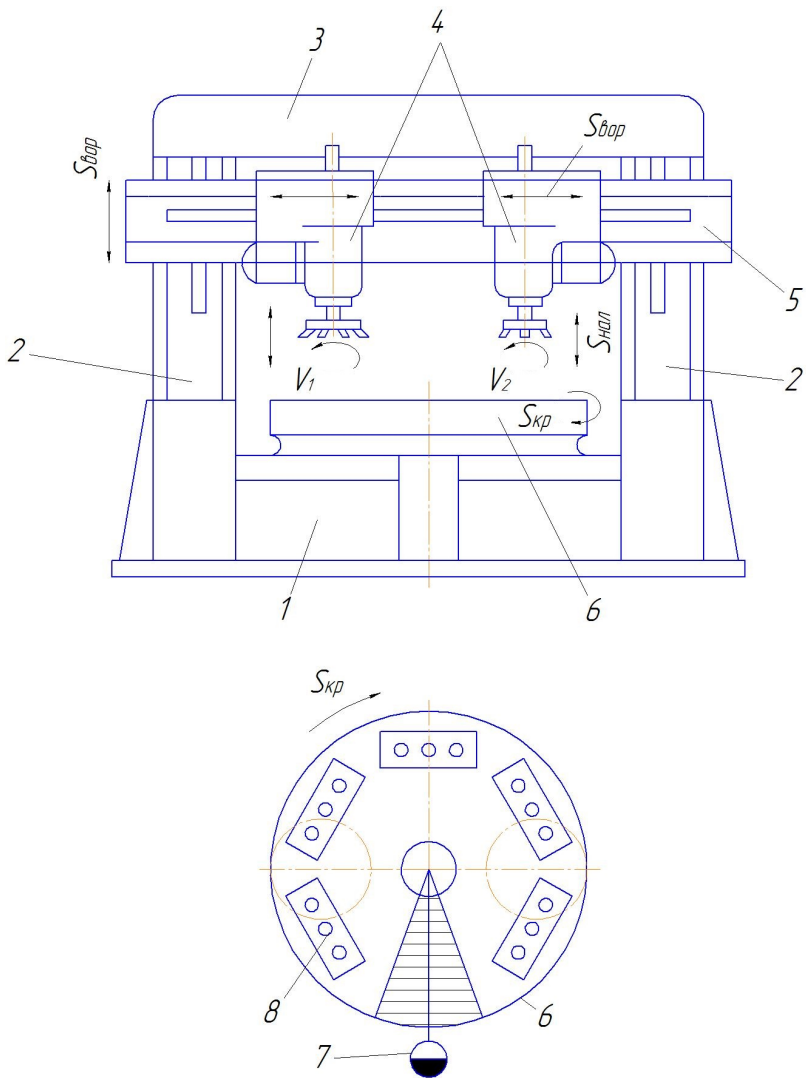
Двухстоечный карусельно-фрезерный станок
